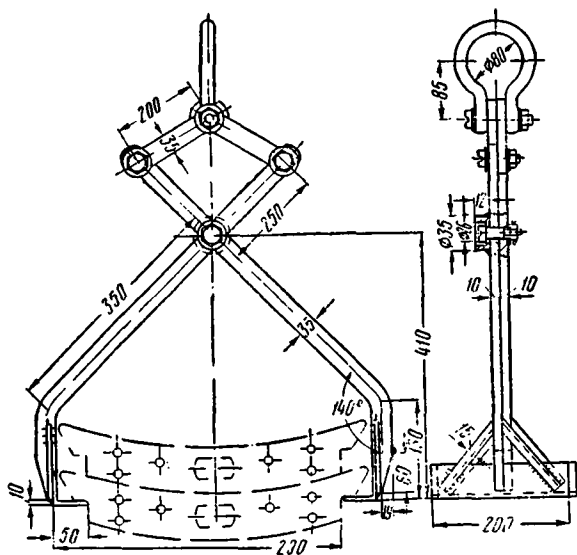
Приспособление для транспортирования сердечников полюсов и катушек
